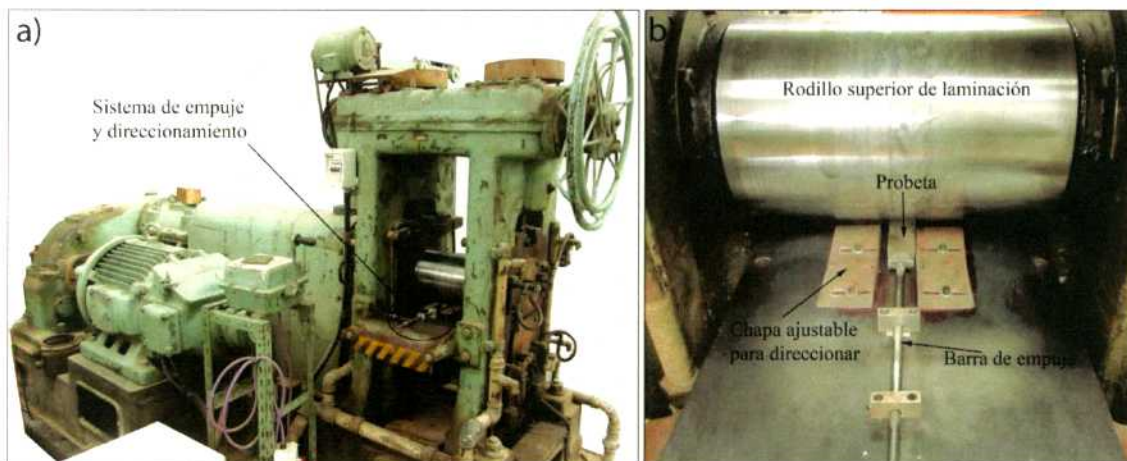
a) *Máquina laminadora FRIED.KRUPP.* b) *Detalle del dispositivo para alinear probetas.
